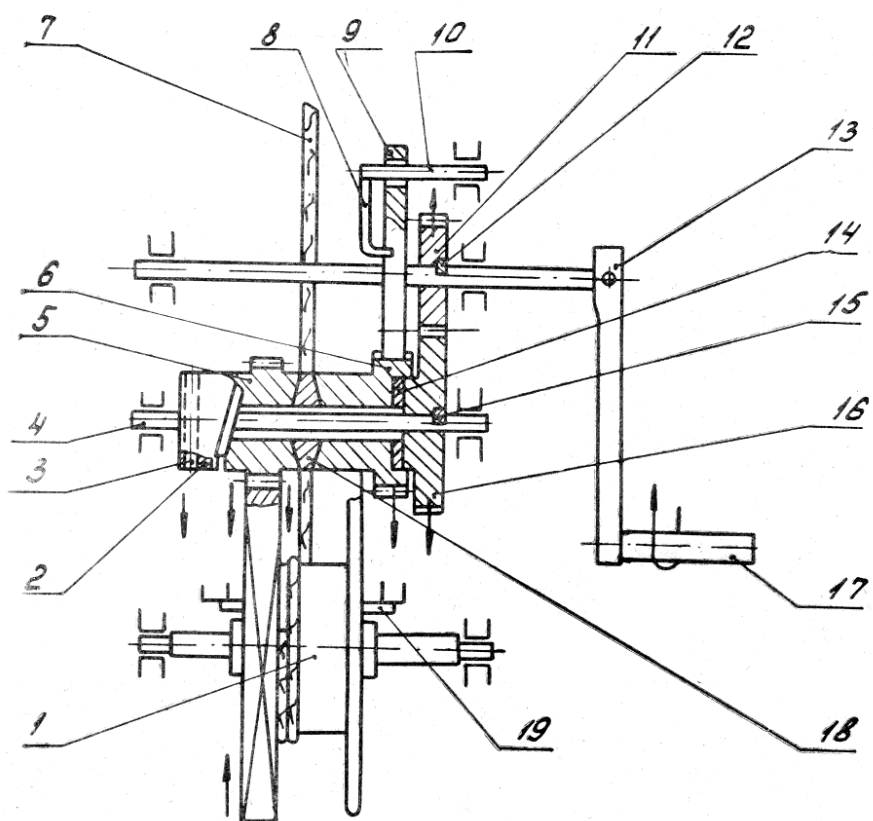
Схема механизма лебедки (стрелки показывают направление движения при разворачивании мачты):
